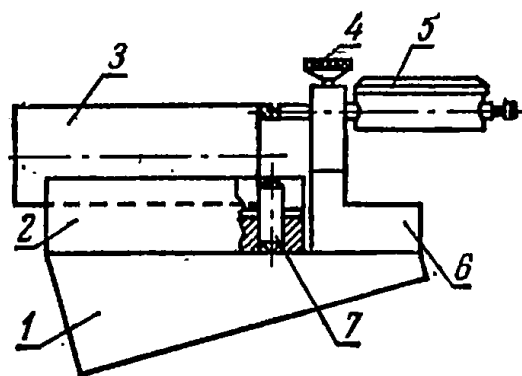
Приспособление для контроля биения торца поршневых пальцев:
